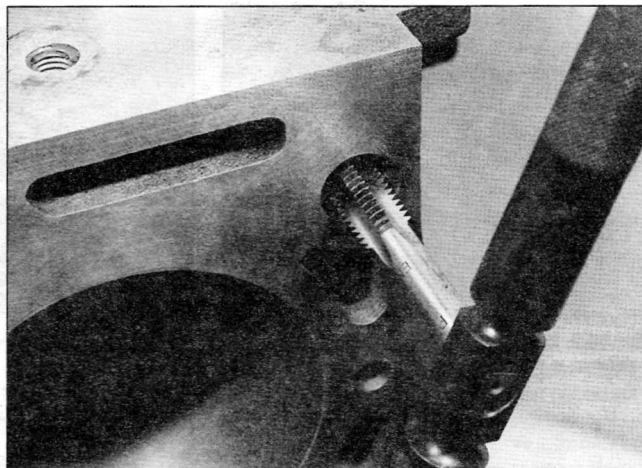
Используйте подходящий метчик для очистки резьбовых отверстий в блоке цилиндров
